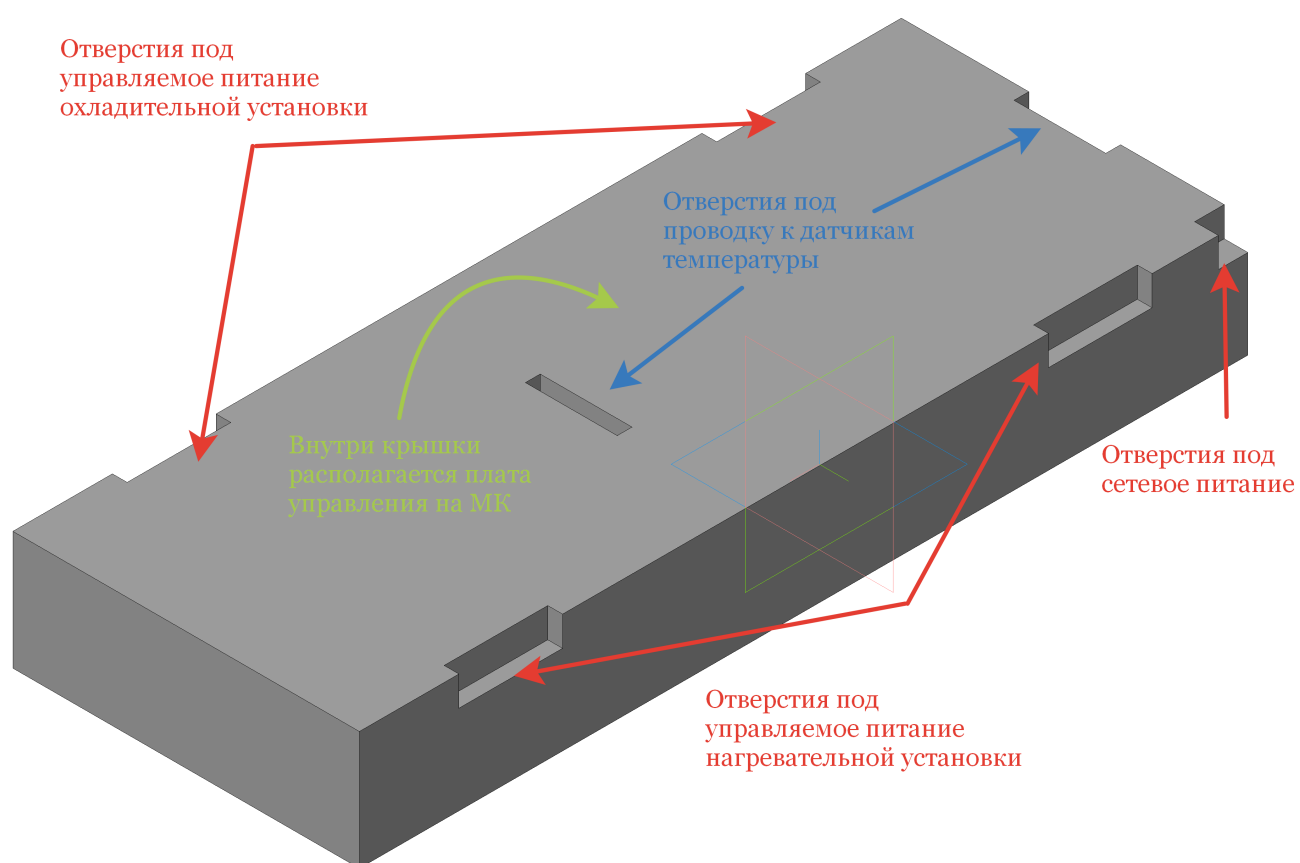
Трёхмерный эскиз "крышки" основного стенда проверки термопары
